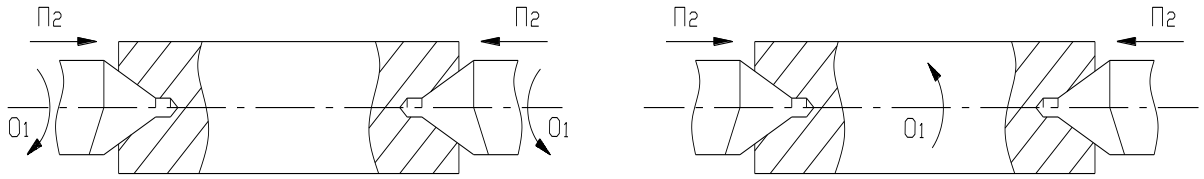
Схема обробки отворів центральними сверлами з рухомою (б) і нерухомою (а) заготовкою
